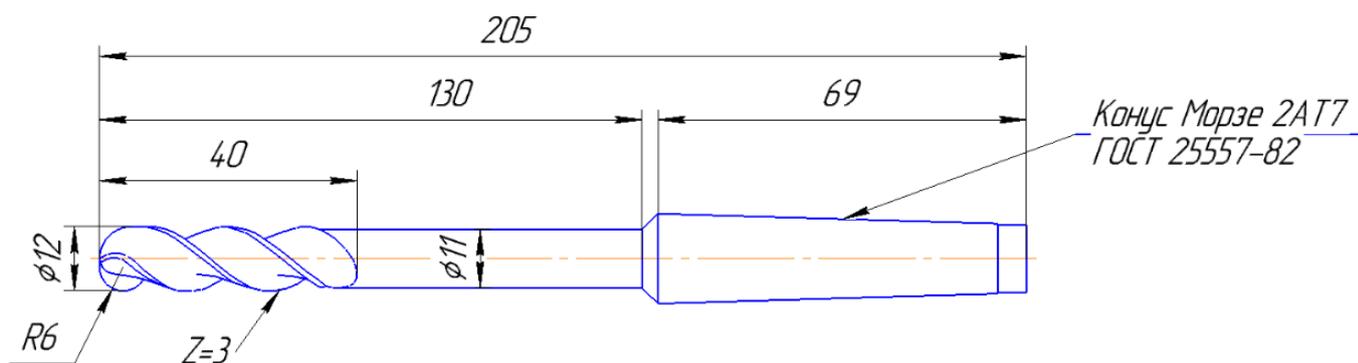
Фреза из быстрорежущей стали Р6М5
